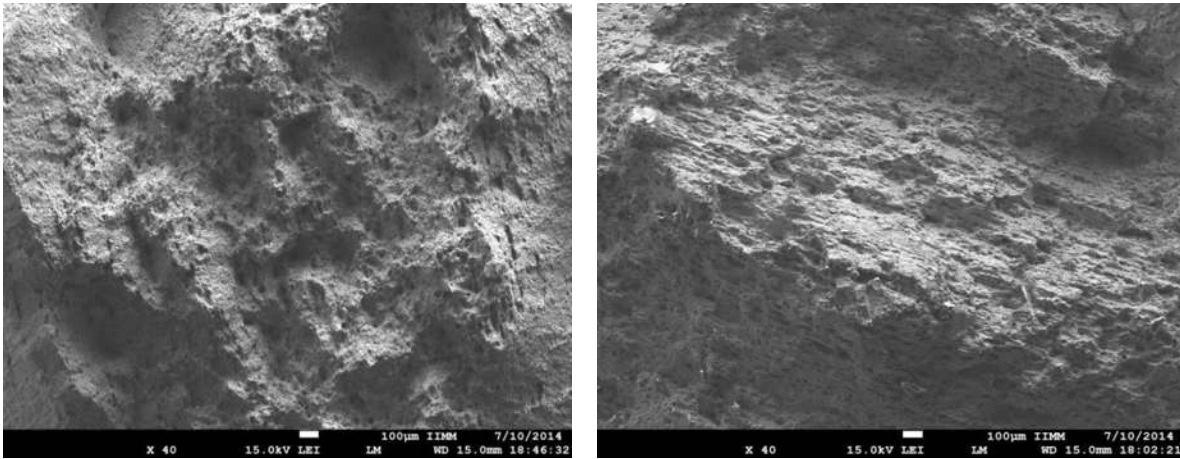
20.-Fractografía de la soldadura 2-1(cordón de auto-revenido, condición 1).
